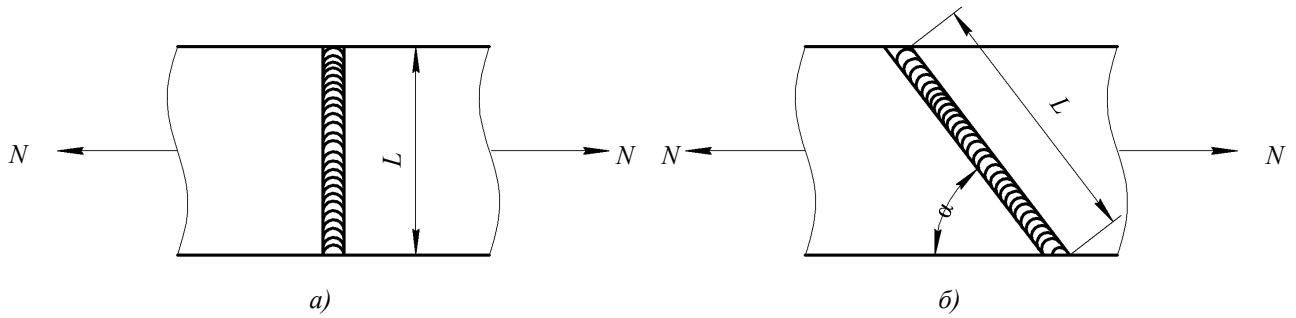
Типы сварных соединений: *a* — цилиндрическая соединяемая поверхность; *б* — коническая соединяемая поверхность; *N* — нагрузка; *L* — длина сварного шва; α — угол соединяемых поверхностей
